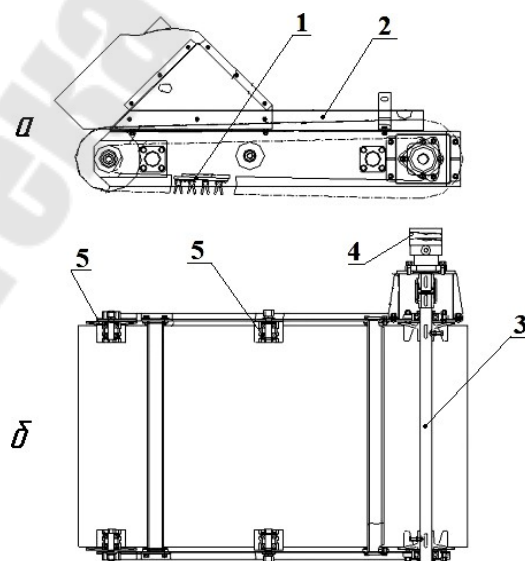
Верхняя наклонная горка: а – вид сбоку, б – вид сверху; 1 – транспортер отдельный; 2 – рама; 3 – вал ведущий; 4 – гидромотор; 5 – ролики поддерживающие
